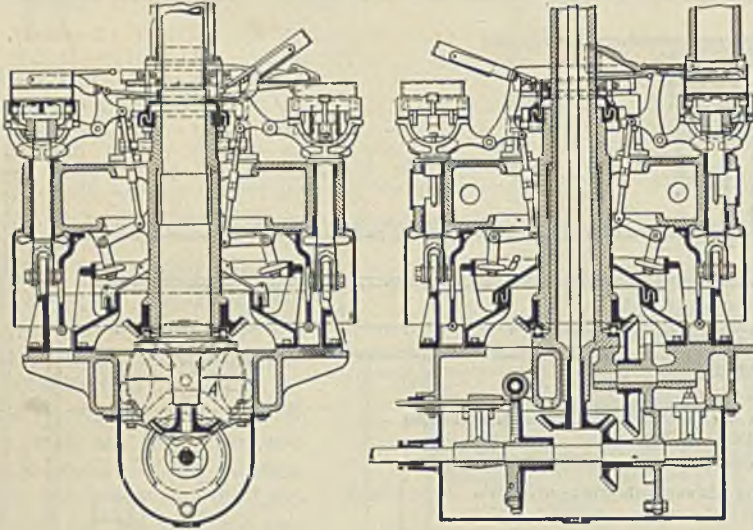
und 4. Querschnitt durch eine frühere Ausführung der Formmaschinen.
